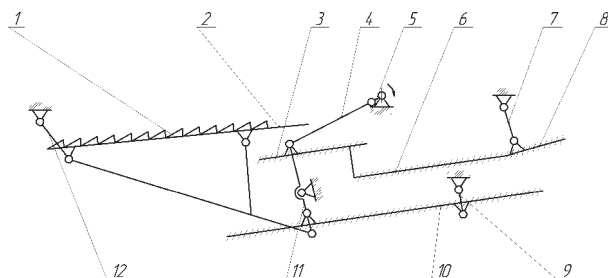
Схема очистки зерноуборочного комплекса «Полесье-Ротор»: 1 — стрясная доска; 2 — пальцевая решетка; 3 — дополнительное решето; 4 — шатун; 5 — кривошип; 6 — верхнее решето; 7, 9, 12 — шарнирные подвески; 8 — удлинитель верхнего решета; 10 — нижнее решето; 11 — двуплечий рычаг
